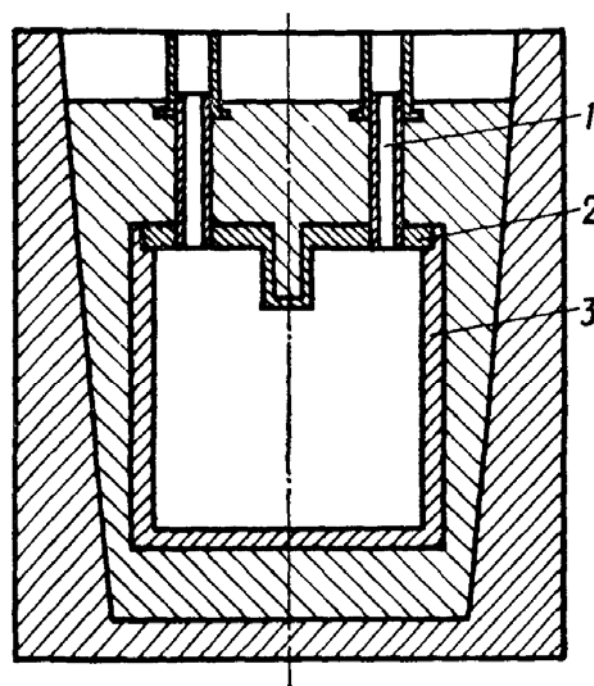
Схема приспособления для изготовления резонатора методом литья:
